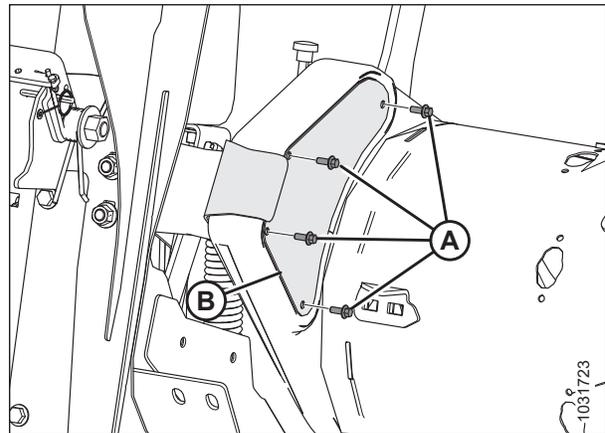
Linke Seite des Einzugsschnecke-Getriebes – Rückansicht
